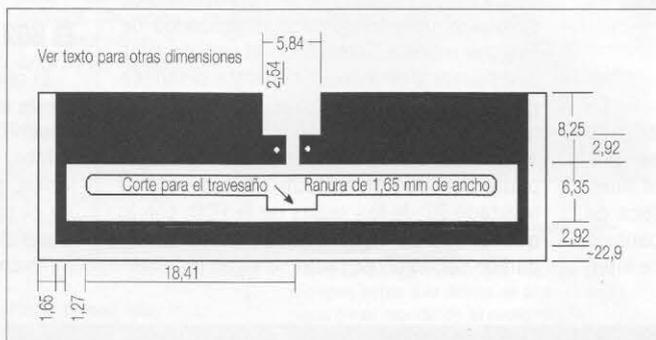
Dimensiones en milímetros de la zona atacada del elemento excitado. Está fabricado sobre una placa de circuito impreso de una sola cara sobre cerámica, de 1,6 mm de grueso. El conductor central y la malla del coaxial se sueldan directamente en cada uno de los orificios centrales.
